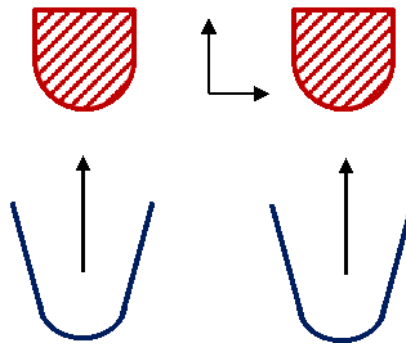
Encaixes para centrar molde com eixo zero da máquina
